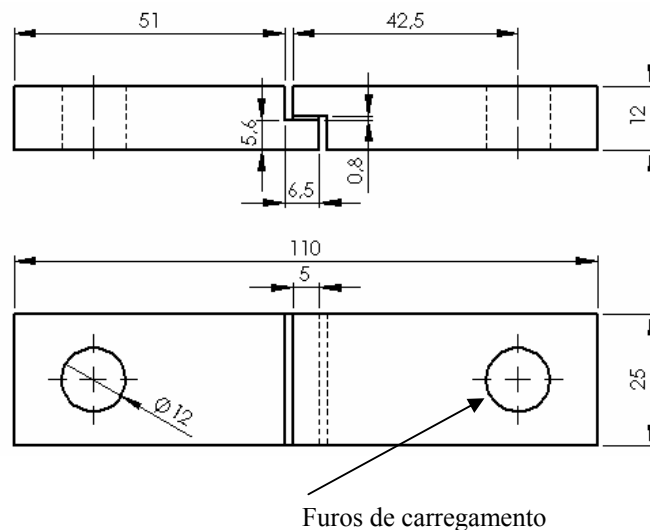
Provette TAST, segundo ISO 11003-2.2 (dimensões em mm).
